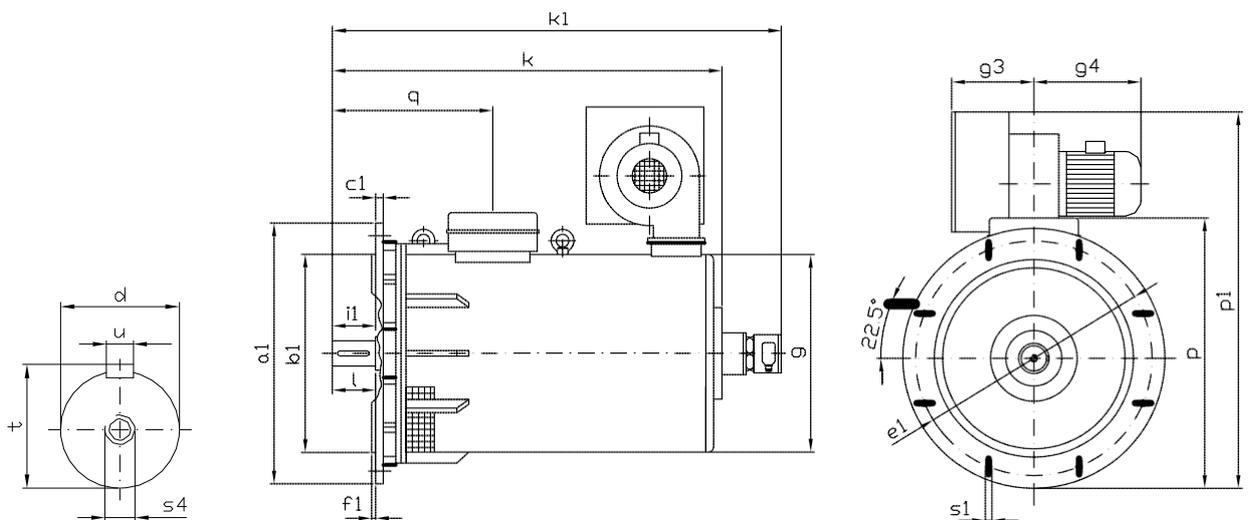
Drehstrom-Käfigläufermotor mit Encoder mit Anbauflansch: Kühlung IC 06, Schutzart: IP 23, Bauform: IM B5
